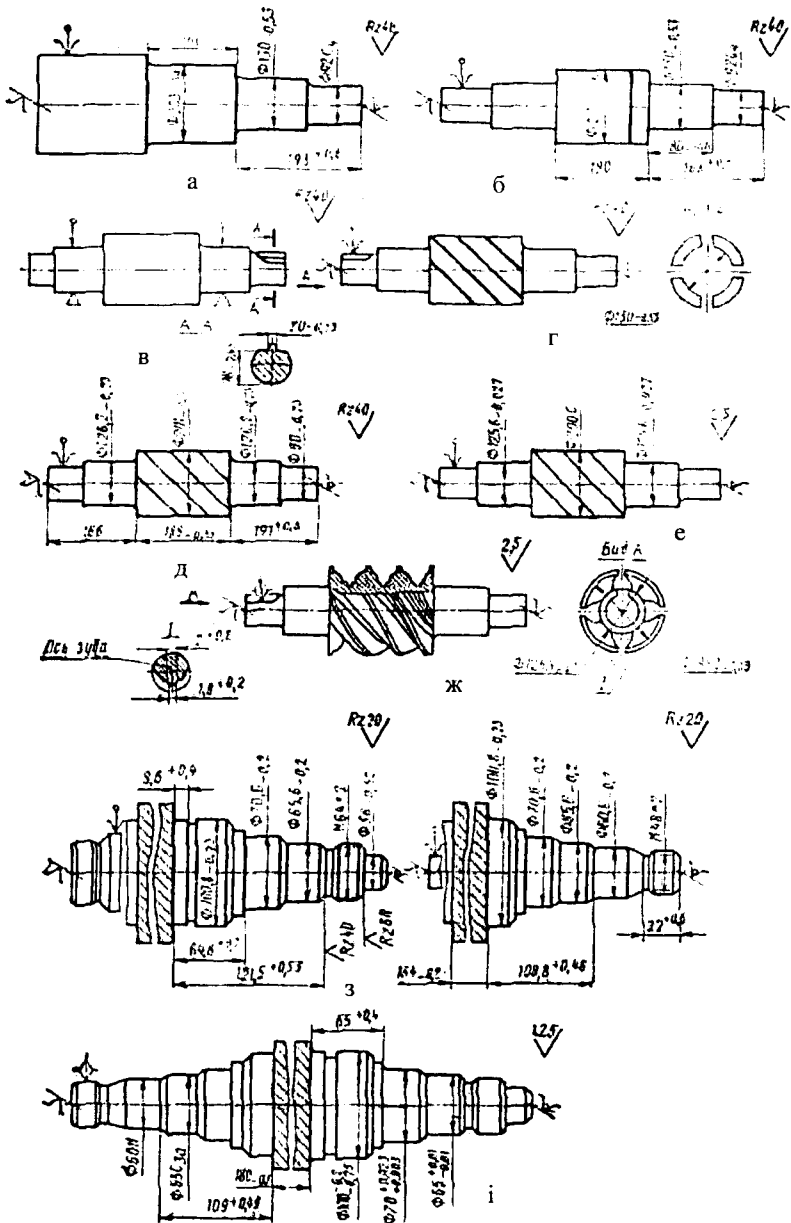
Технологічна схема механічної обробки ротора гвинтового компресора 14ВК.
